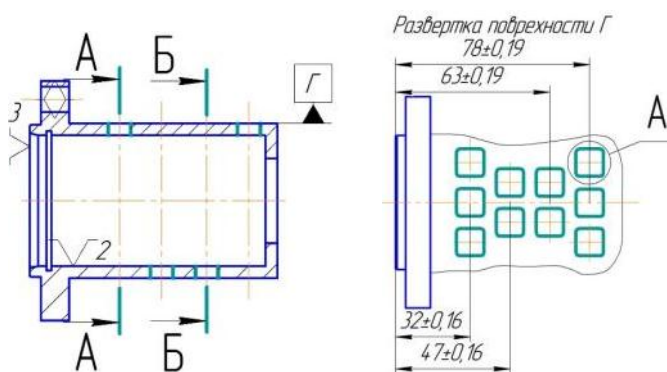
Эскиз координатно-расточной операции с ЧПУ
